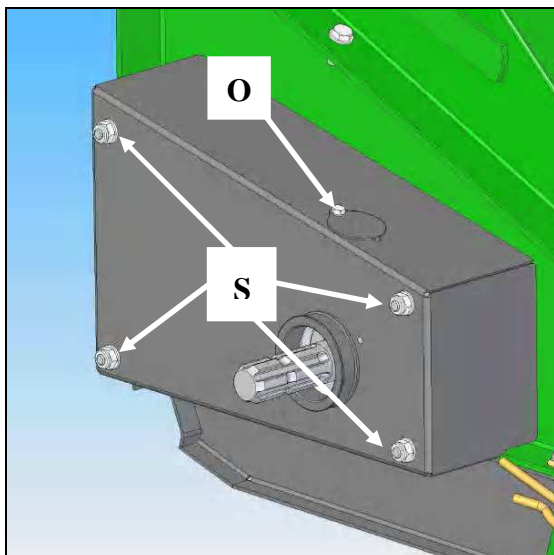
а. Защитный кожух приводной цепи Рис.22б. Регулировка натяжения цепи привода впускателя
